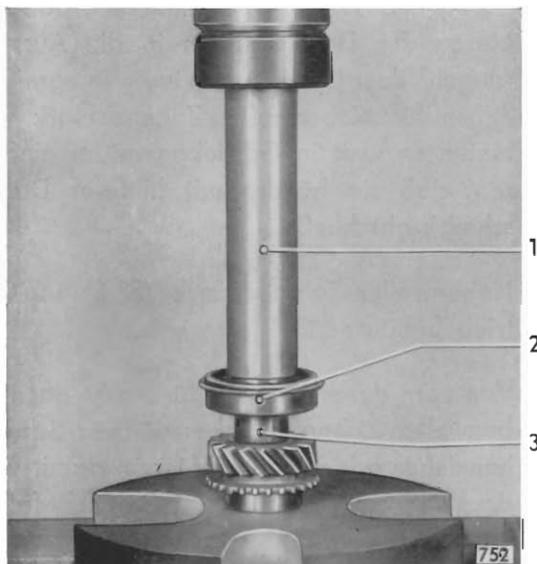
Kugellager auf Hauptantriehrad aufdrücken
